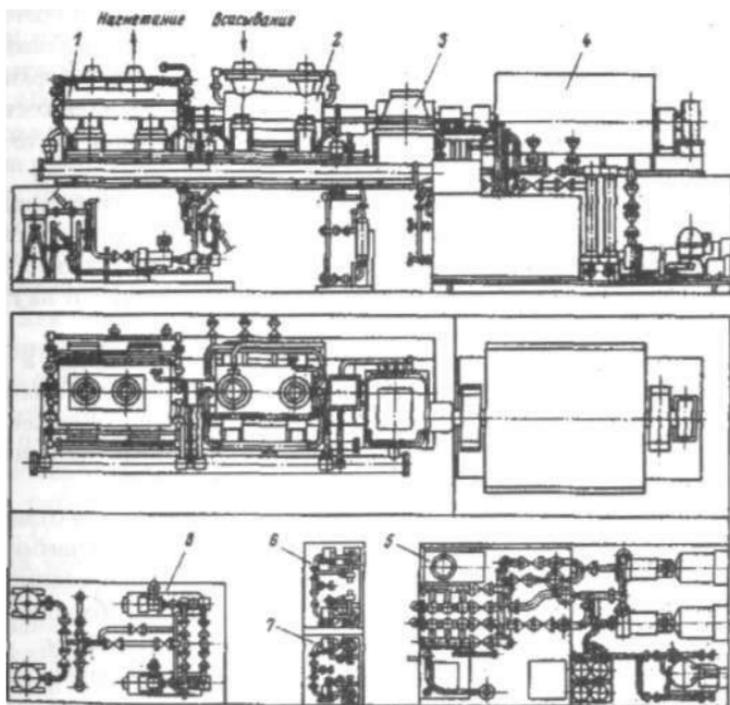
Центробежный компрессор 43ГЦ2-100/5-100:
